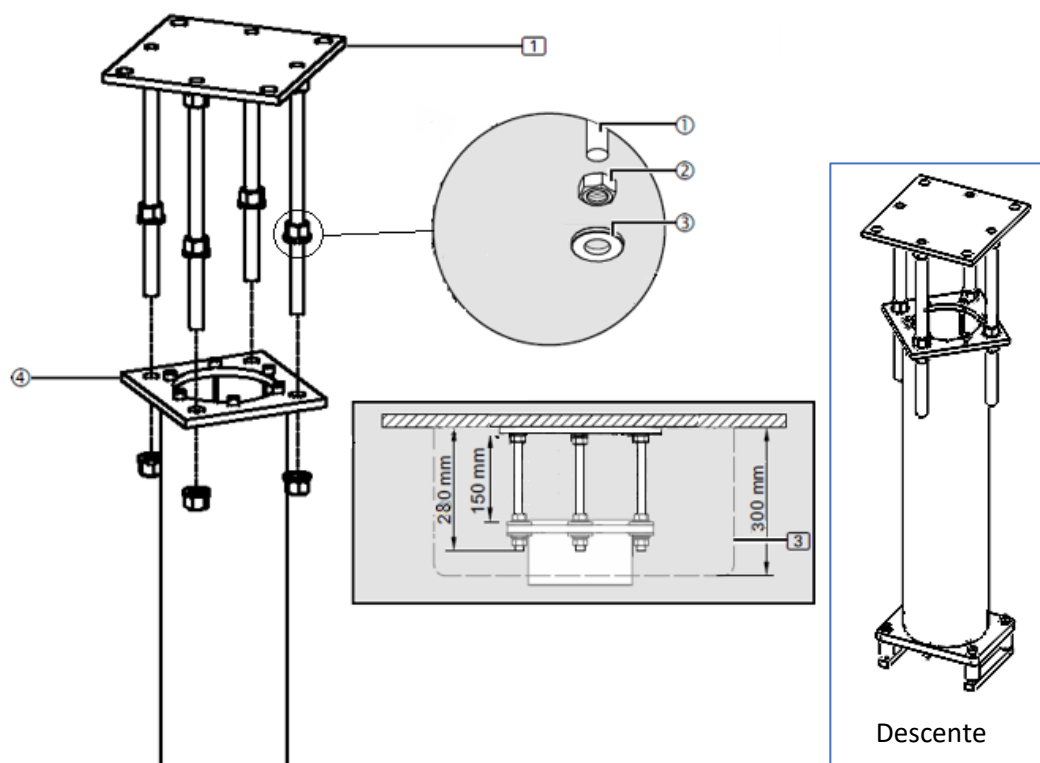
Installation du tuyau de descente sur la plaque d'interface
